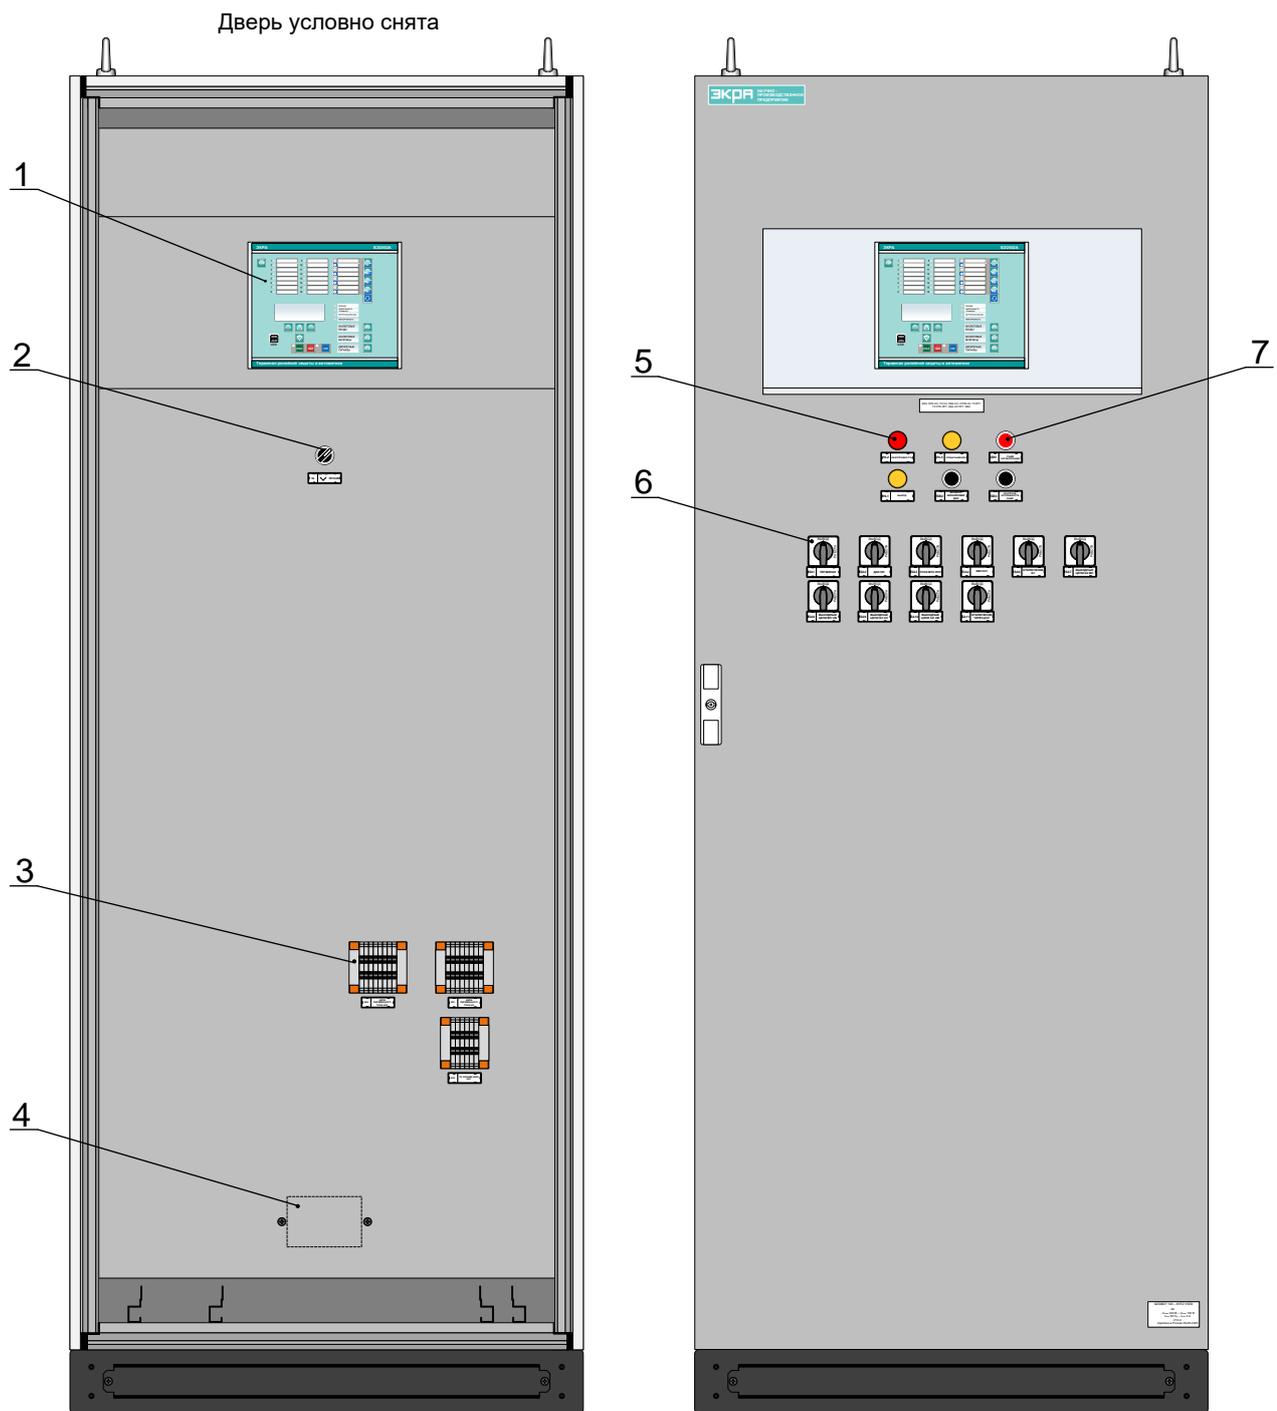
Общий вид шкафа ШЭ2607 143.
